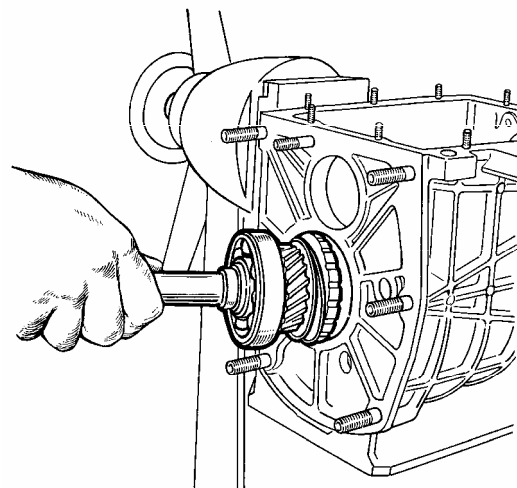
Извлечение первичного вала из картера коробки передач
